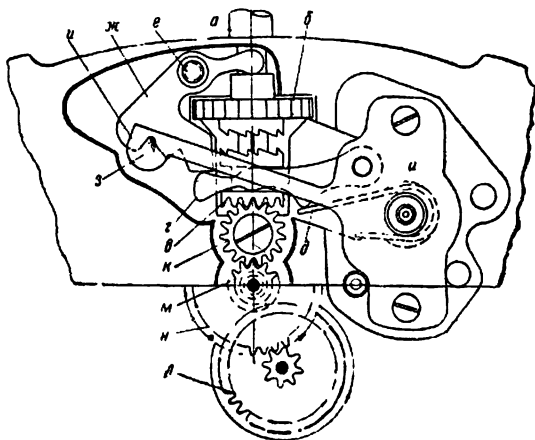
Ремонтуар часов марки «Звезда» в положении перевода стрелок: а — заводной вал; б — заводной триб; в — кулачковая муфта; г — заводной рычаг; д — пружинка заводного рычага; е — винт переводного рычага; ж — переводной рычаг; з — штифт фиксатора; и — фиксатор (мост ремонтуара), к — переводное колесо; л — вексельное колесо с трибом; м — минутный триб; н — часовое колесо
